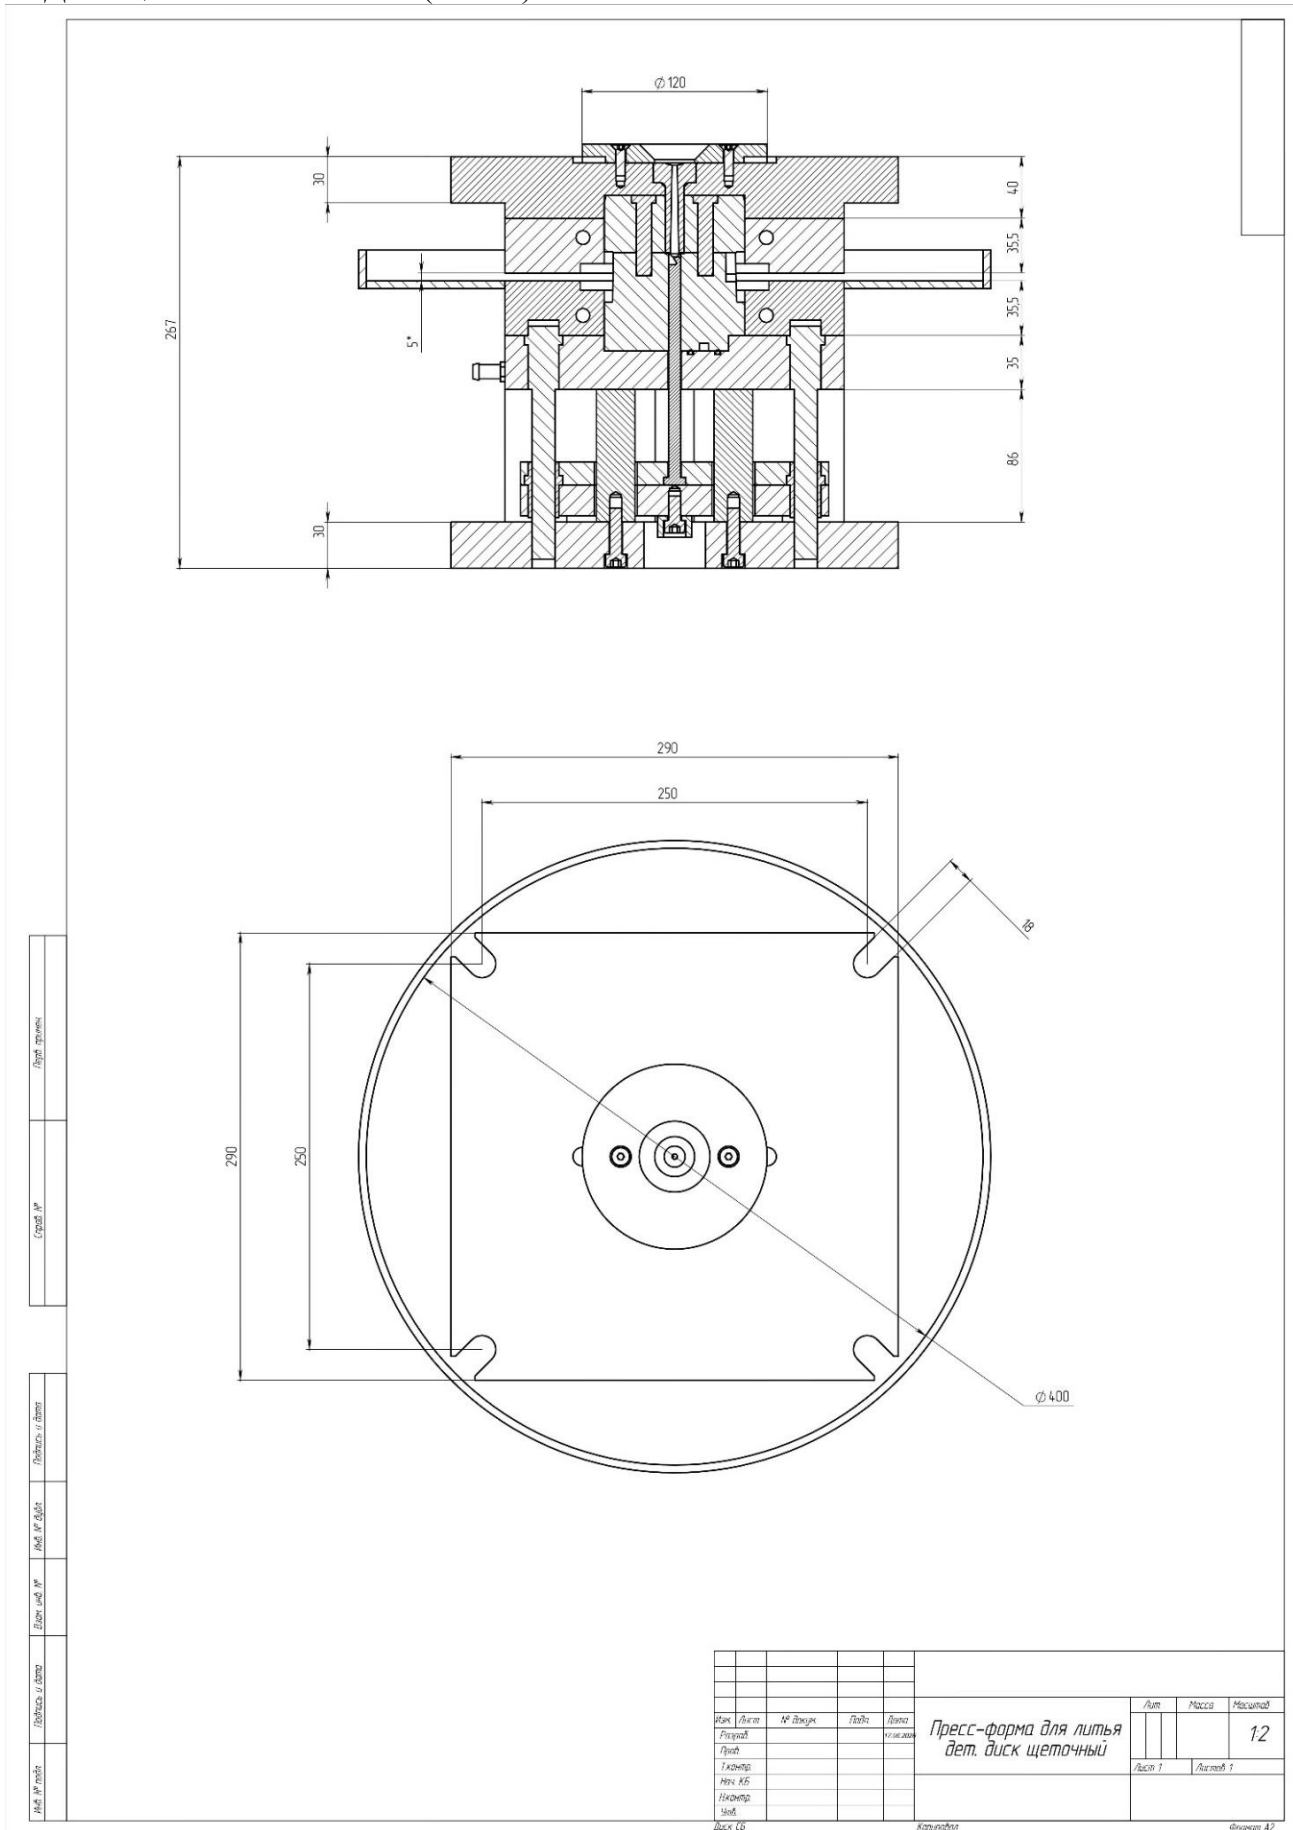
Чертеж пресс-формы для литья диска щеточного.
